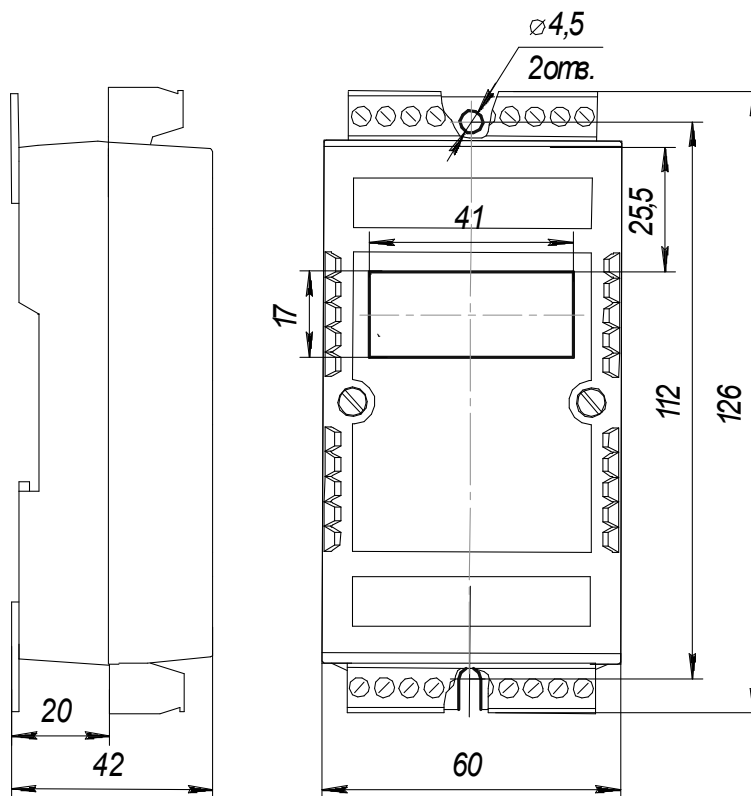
Габаритные и присоединительные размеры преобразователя ПИТ
